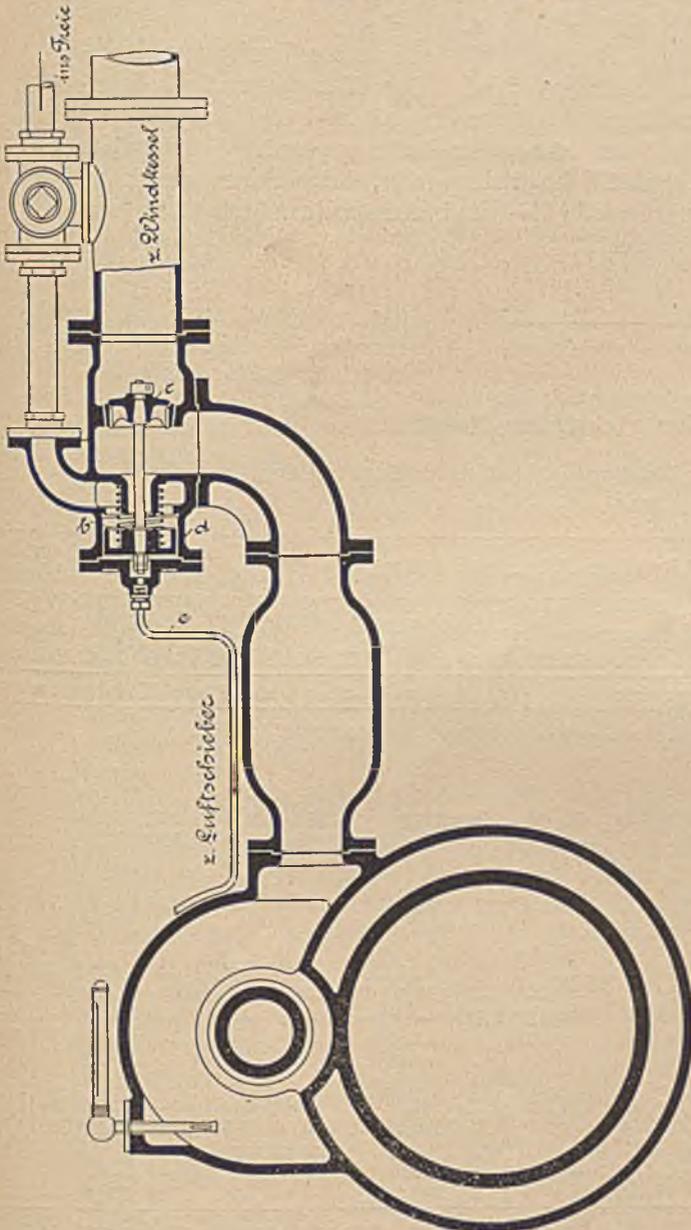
Pneumatische Reguliervorrichtung des Kompressors der Maschinenbau- A.-G. Union in Essen.
